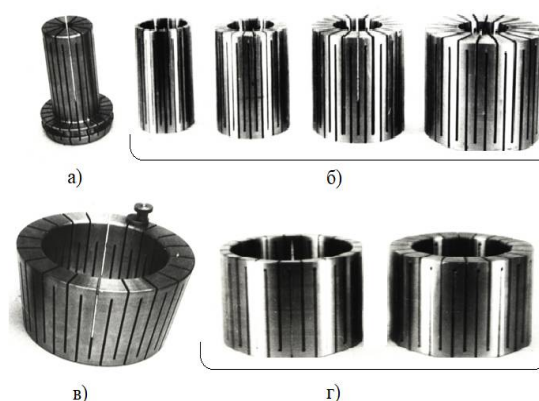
Рабочая оснастка устройства для калибровки: а, б – маточный пуансон и быстрьюемые пуансоны для калибровки труб раздачей; в, г – маточная матрица и быстрьюемые матрицы для калибровки труб обжатием
